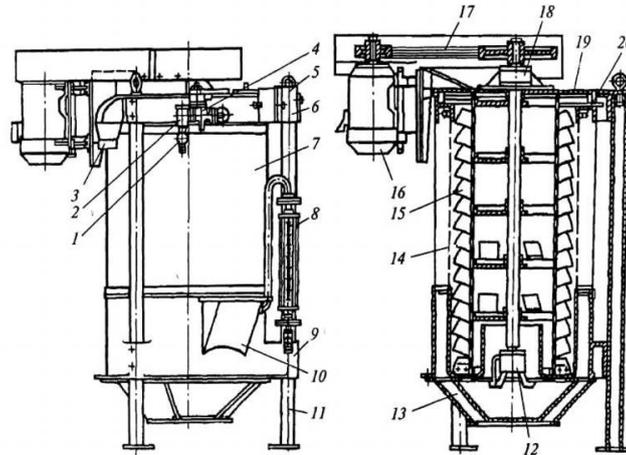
Машина А1-БМШ: 1 – запірний вентиль; 2 – фільтр; 3 – випускний патрубок; 4 – мембранний вентиль; 5 – прилад для контролю подачі води; 6 – траверса; 7 – кожух; 8 – ротаметр; 9 – корпус; 10 – приймальний патрубок; 11 – стійки; 12 – нижній підшипниковий вузол; 13 – кільцевий конічний канал; 14 – лускатий (ситовий) циліндр; 15 – ротор; 16 – електродвигун; 17 – клинопасова передача; 18 – верхній підшипниковий вузол; 19 – кришка; 20 – трубчасте пластмасове кільце.
